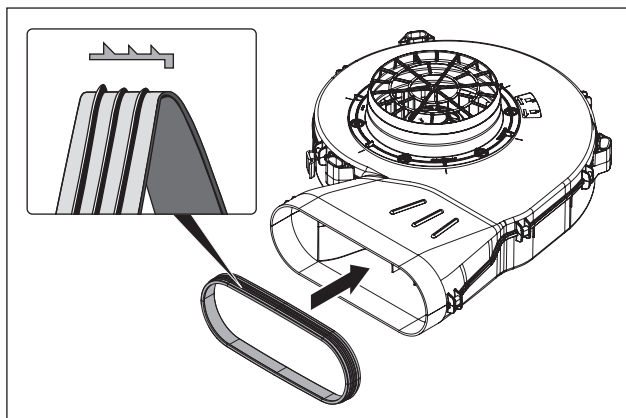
Colocar o vedante na conexão de saída do ventilador de rodapé
